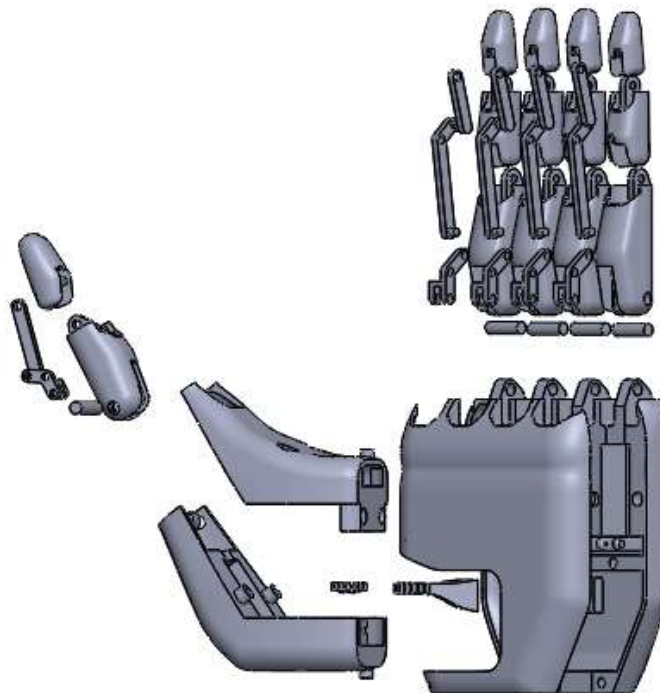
Vista en explosió de totes les parts que conformen la pròtesi. Font: pròpia.
